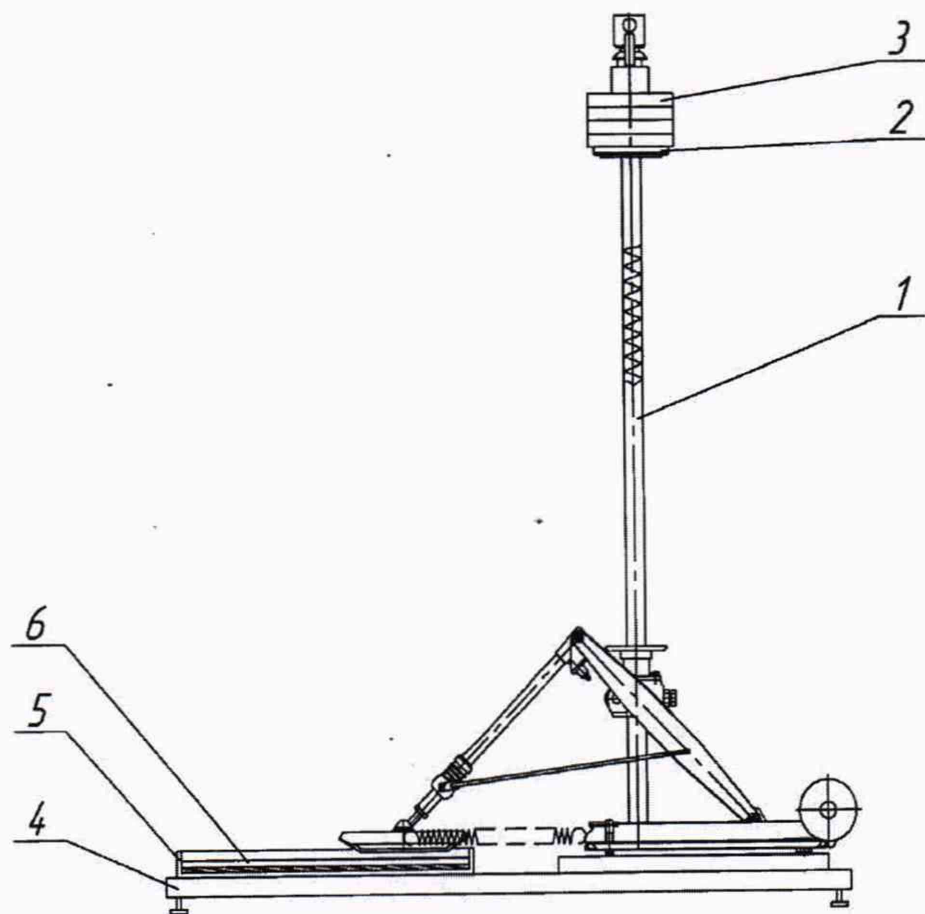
Стенд для поверки ИКСп-2У СДТ 264.00.00.000
